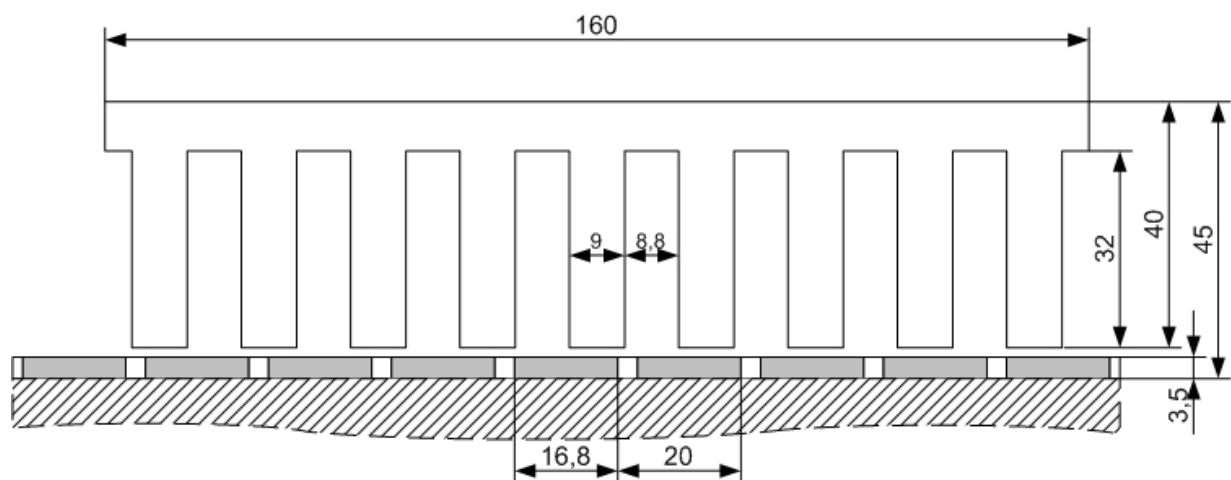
Blechschnitt des bekannten Synchron-Linearmotors (Maß in mm)
